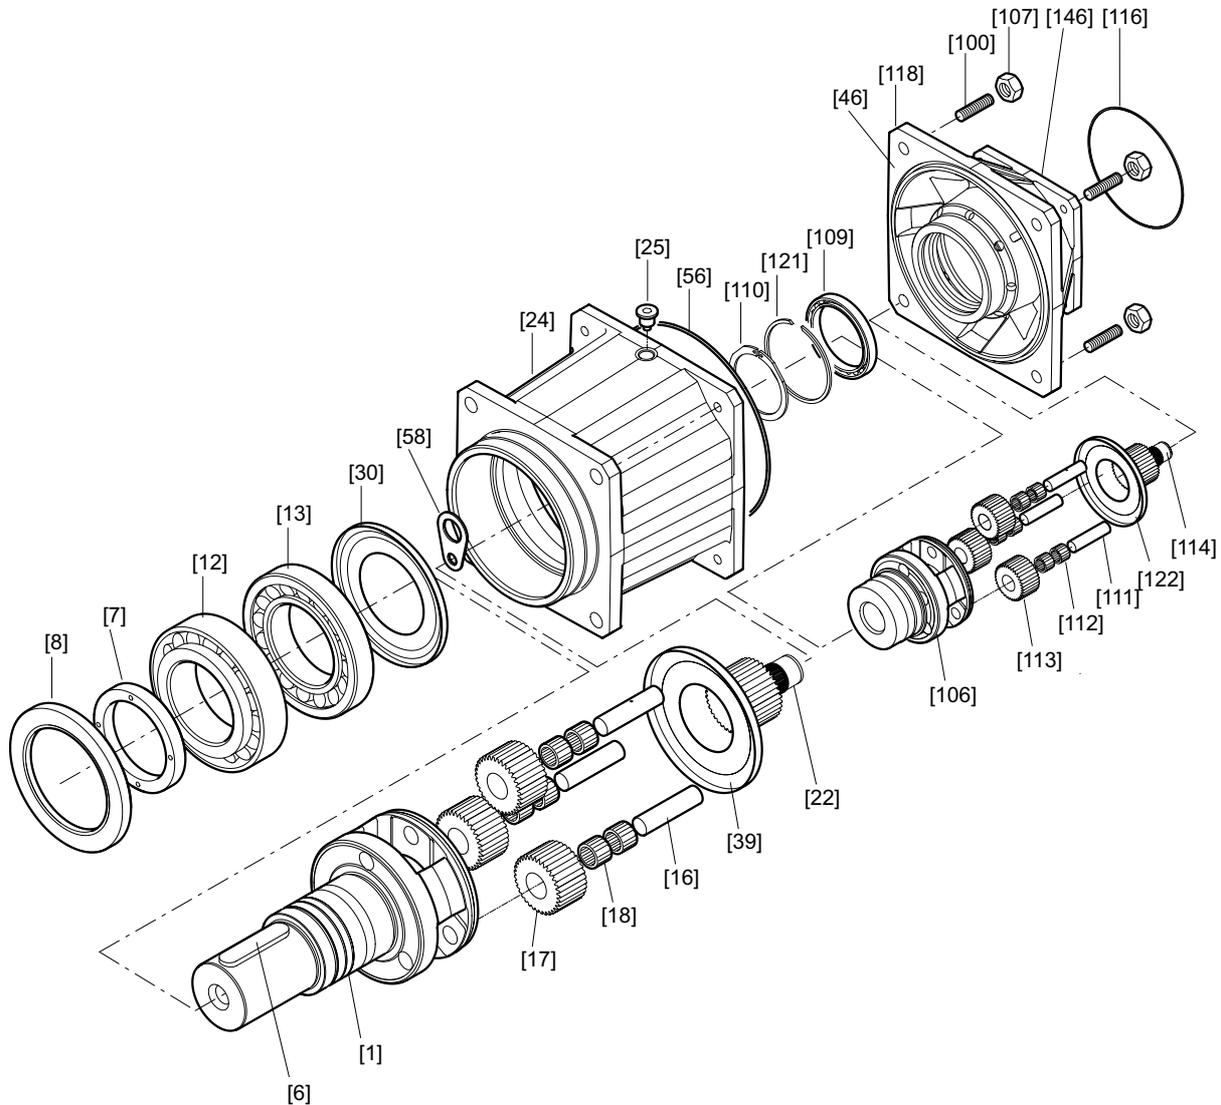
Базовая конструкция планетарных редукторов PSF922 / PSKF922
